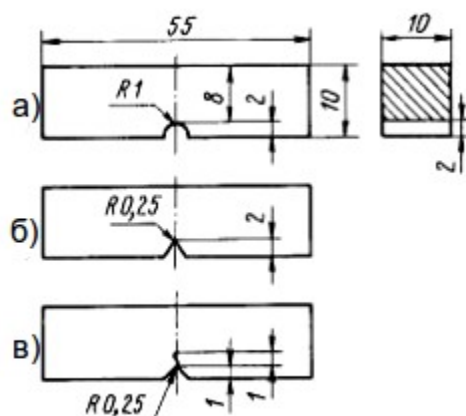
Конструкция образцов для испытаний на ударный изгиб, а) - с U-образным надрезом, б) - с V-образным надрезом, в) - с наведённой трещиной.
